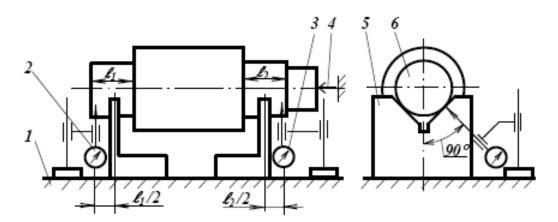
Схема измерения соосности шеек под подшипники шлицевого вала: I – поверочная плита; 2, 3 – измеряемые головки; 4 – упор; 5 – ножевидная призма; 6 – измерительная деталь
